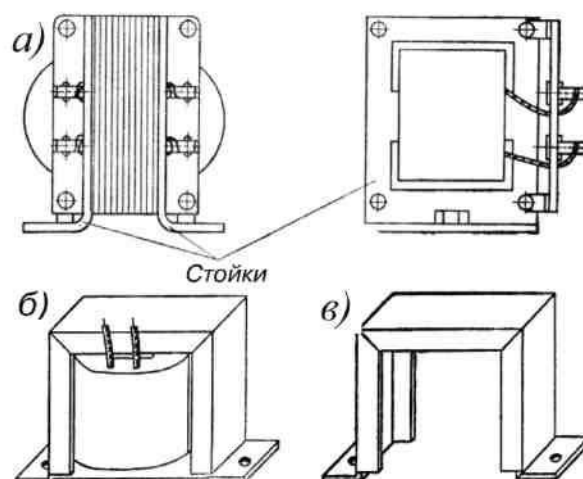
Пластинчатый трансформатор: *а* — с сердечником, стянутым накладными стойками и шпильками; *б* — с запрессованным в обойму сердечником; *в* — обойма
